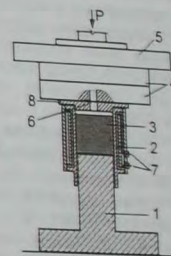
Схема запрессовки шликера в пресс-форму из электрообогреваемого стакана
